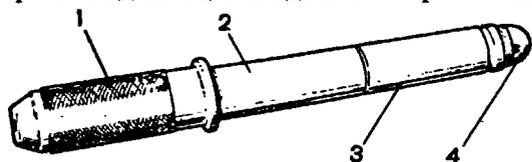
Установка поршневого пальца на приспособление А.60325 для запрессовки его в поршень и головку шатуна: 1 - валик приспособления; 2 - поршневой палец; 3 - направляющая; 4 - упорный винт
